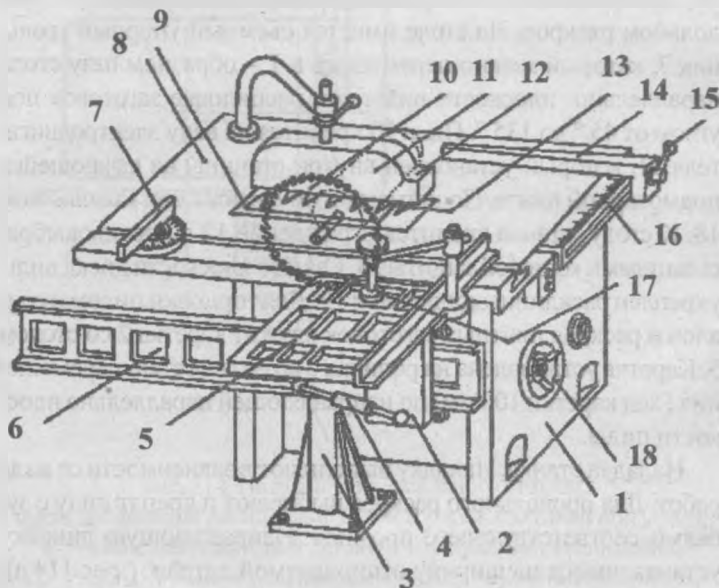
Универсальный круглопильный станок для смешанной распиловки ЦБ-2:
